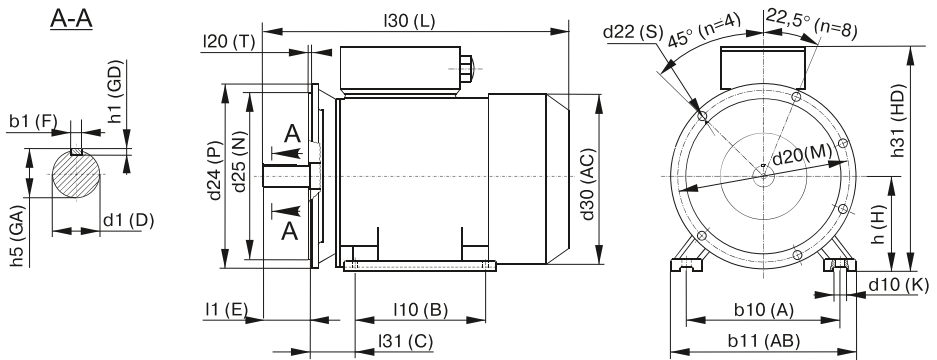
Размеры двигателей монтажного исполнения IM 2081 / Figure 2 – Motor dimensions of IM 2081 mounting version
